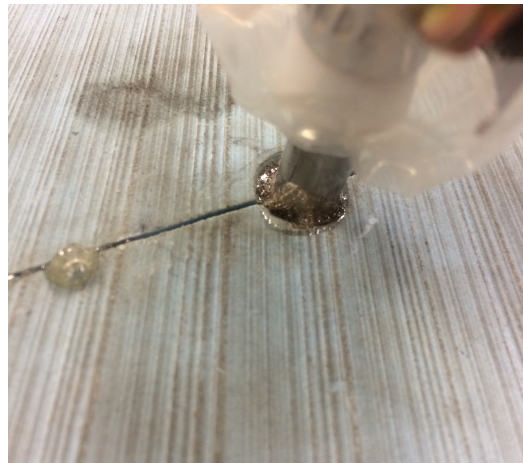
Fabricación II. Exceso de resina en la conexión del tubo y el molde. (Fuente: Propia)
